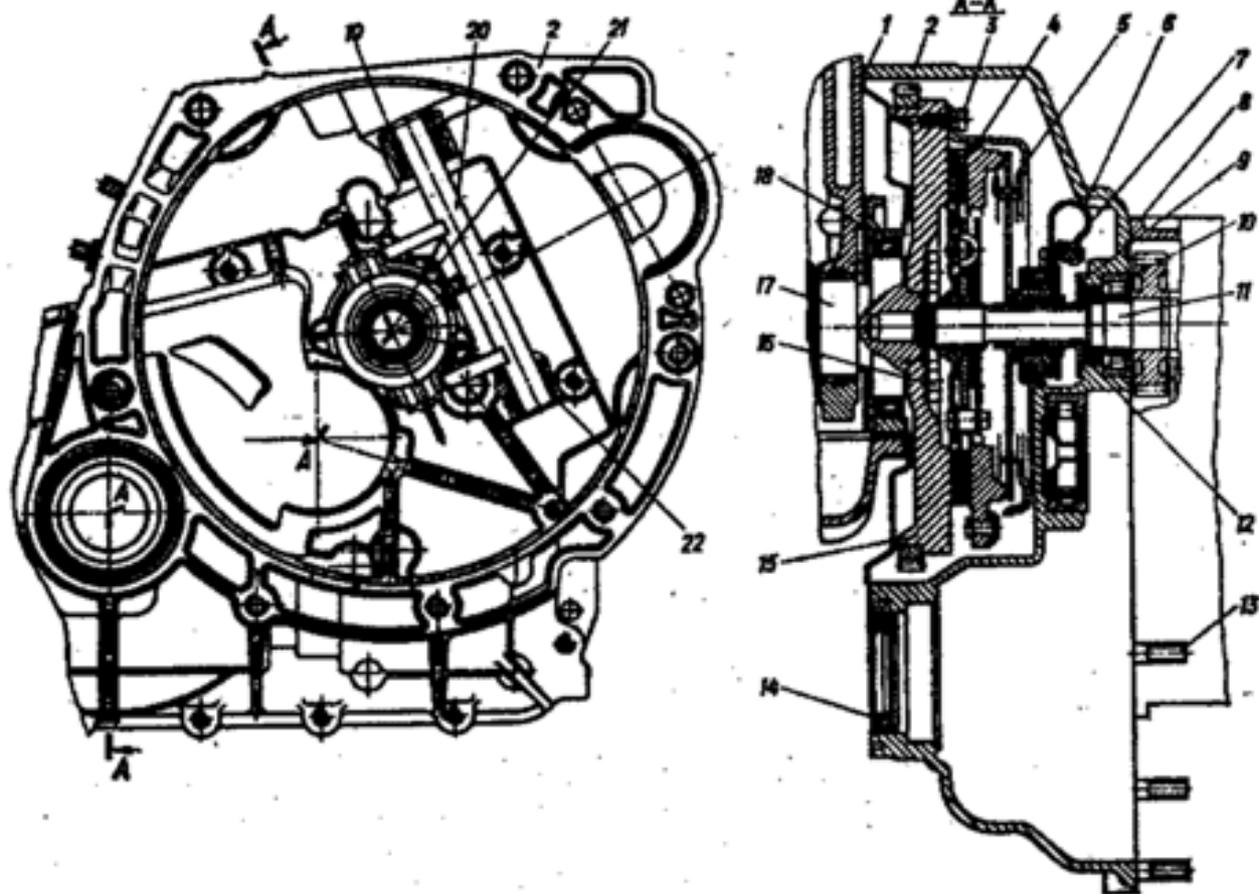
Сцепление: 1 - кожух защитный; 2 - картер сцепления; 3 - болт; 4 - диск сцепления ведомый; 5 - диск сцепления нажимной; 6 - звено соединительное; 7 - подшипник выключения сцепления; 8 - картер коробки передач; 9 - втулка направляющая с фланцем; 10 - подшипник роликовый ведущего вала коробки передач; 11 - вал ведущей коробки передач; 12 - манжета ведущего вала; 13 - шпилька; 14 - манжета дифференциала; 15 - маховик; 16 - болт крепления маховика; 17 - вал коленчатый; 18 - манжета коленчатого вала; 19, 22 - втулка вилки выключения сцепления; 20 - вилка выключения сцепления; 21 - винт
